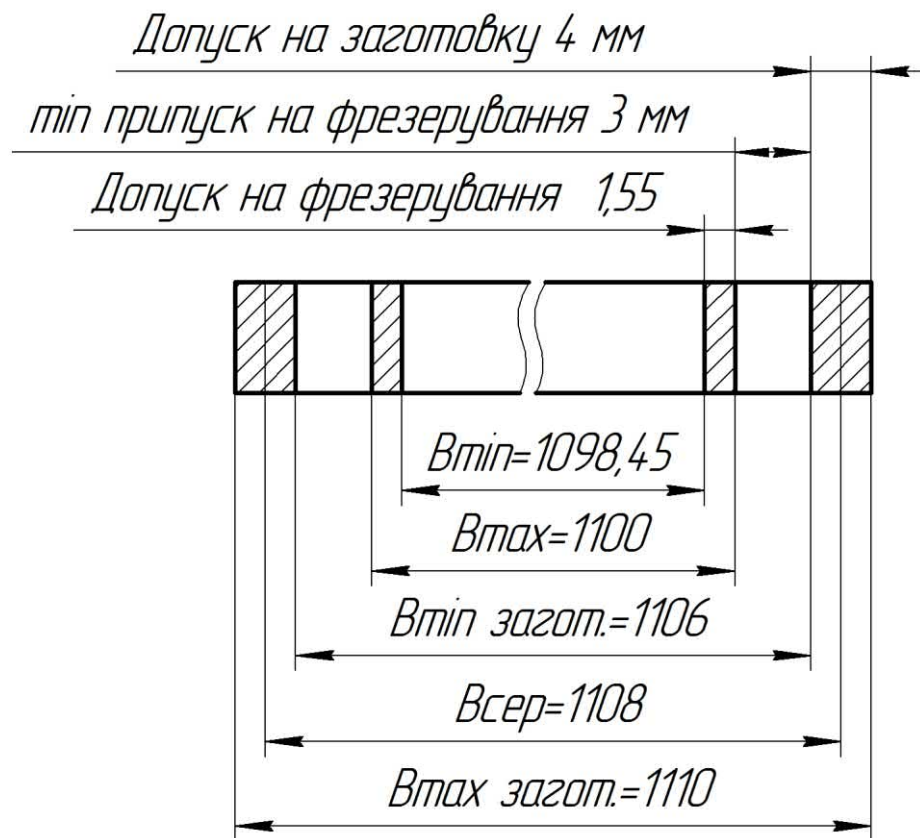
Схема розташування припусків і допусків на механічну обробку поверхні розміром 1100 h14
